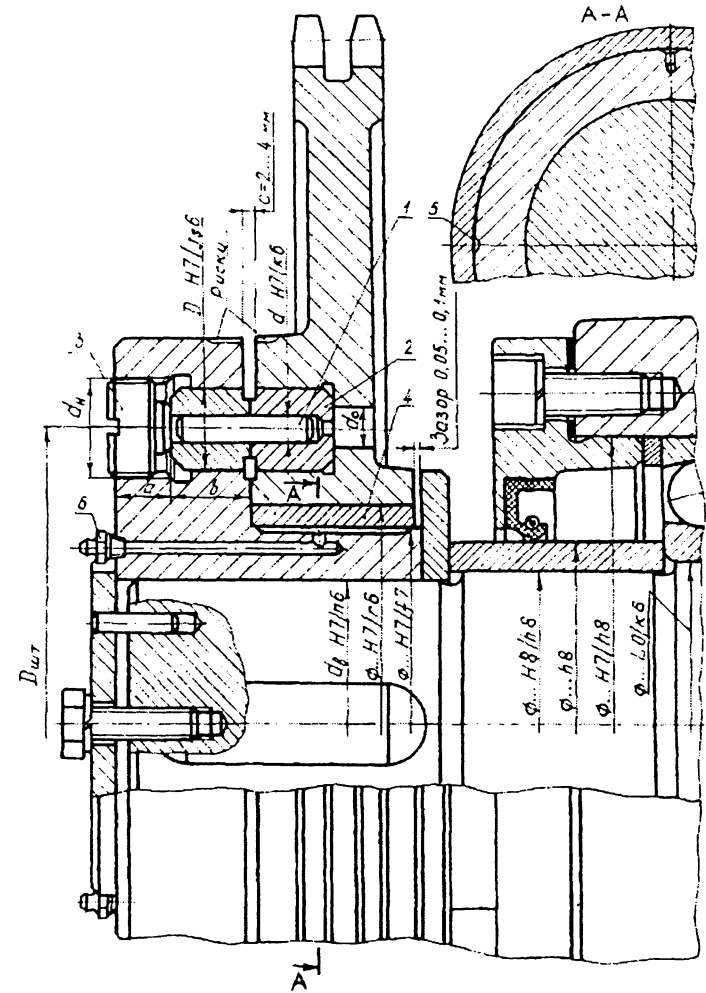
Ведомая звездочка с предохранительным устройством: 1 – штифт; 2 – стальная закаленная втулка; 3 – резьбовая пробка; 4 – подшипниковая бронзовая втулка; 5 – смазочная канавка; 6 – пресс-масленка
